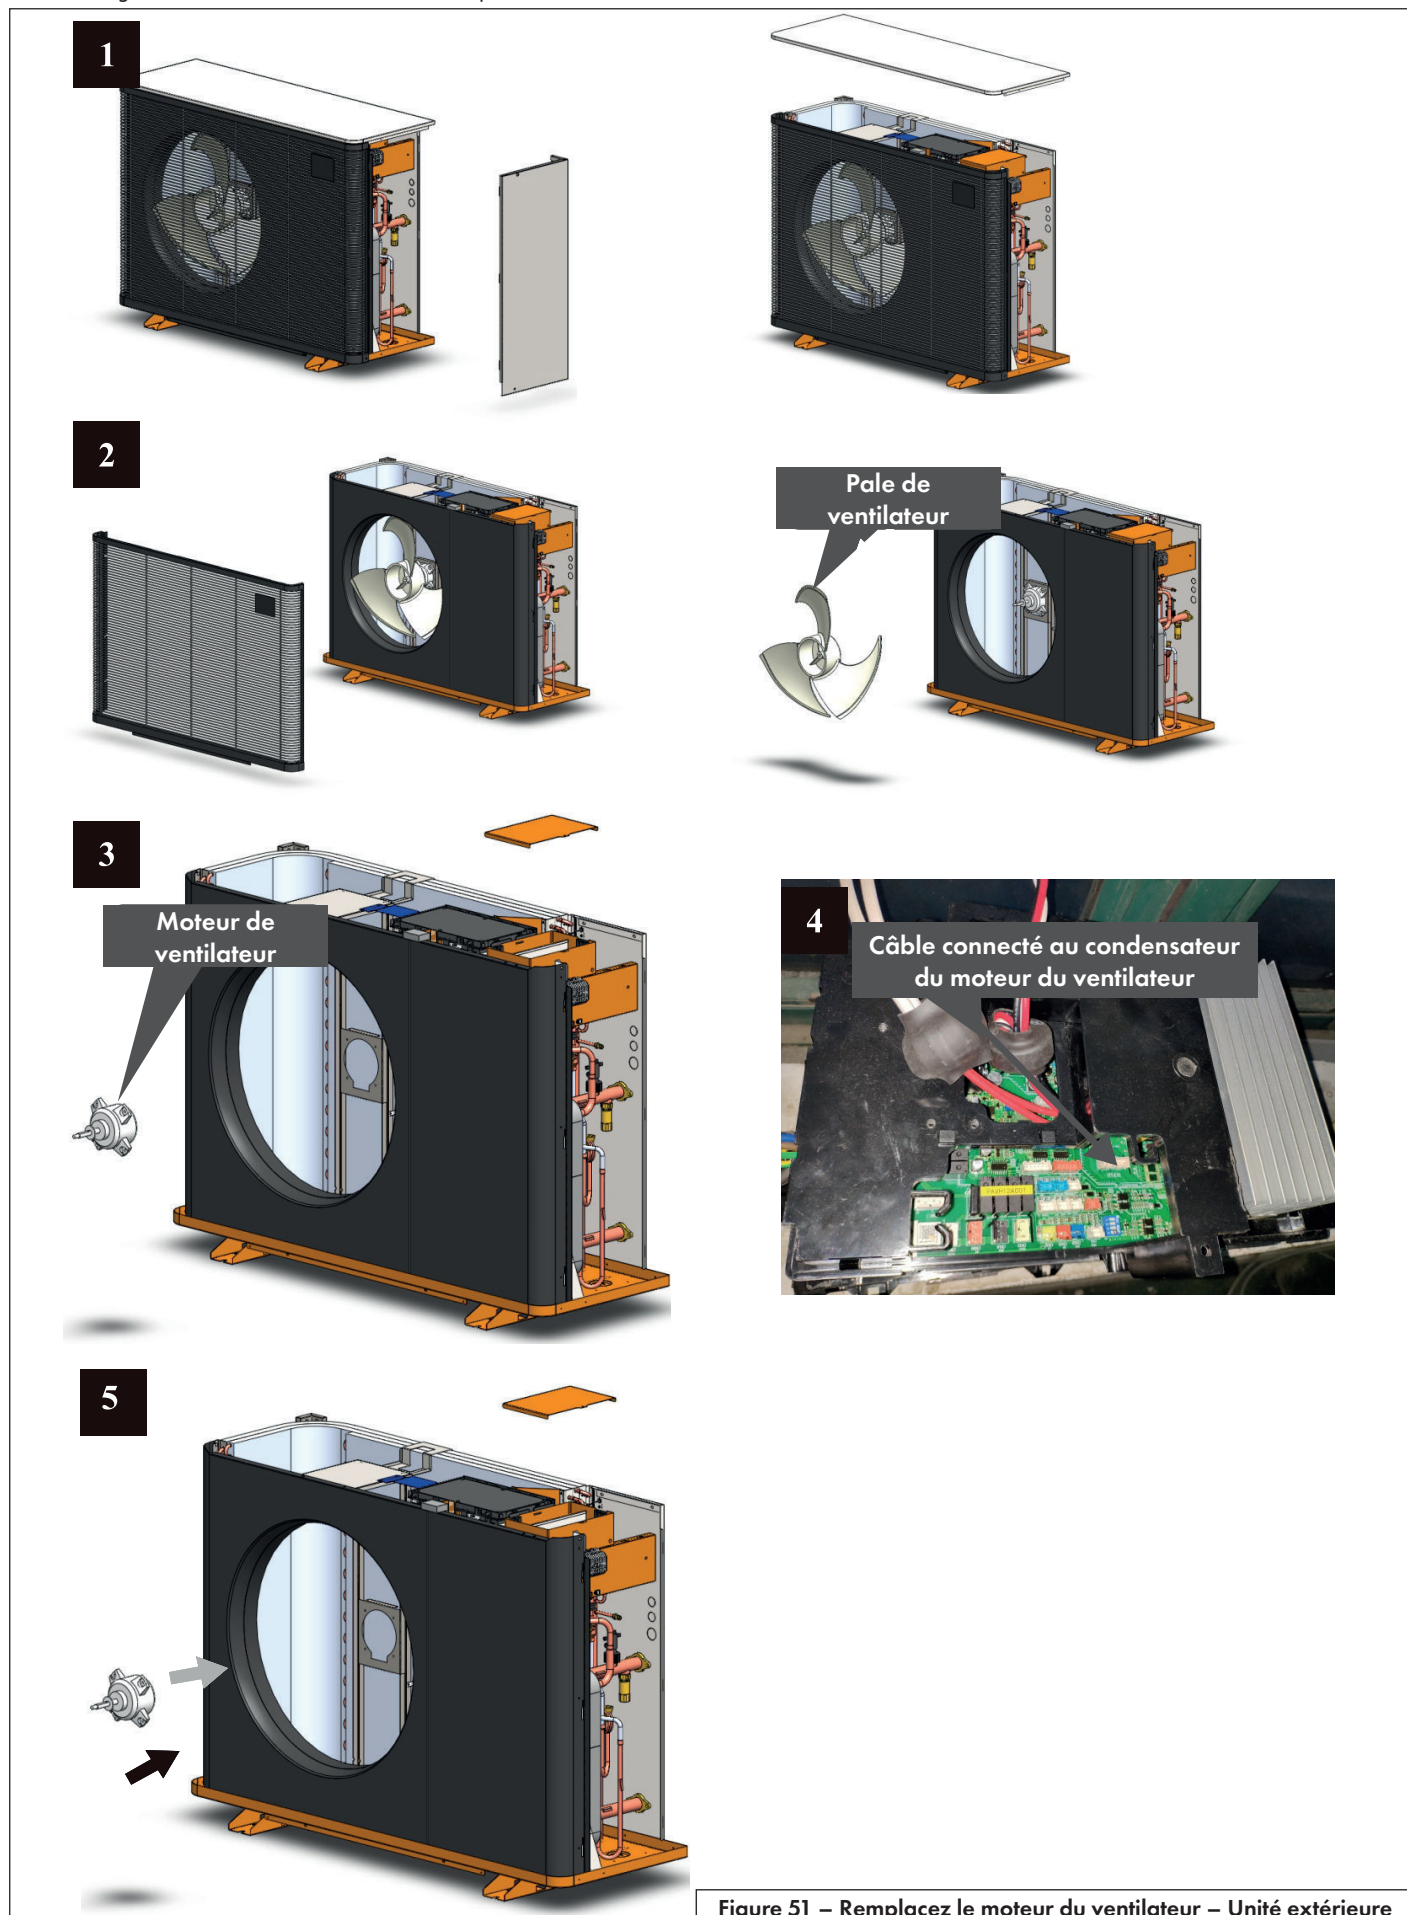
Remplacez le moteur du ventilateur – Unité extérieure
